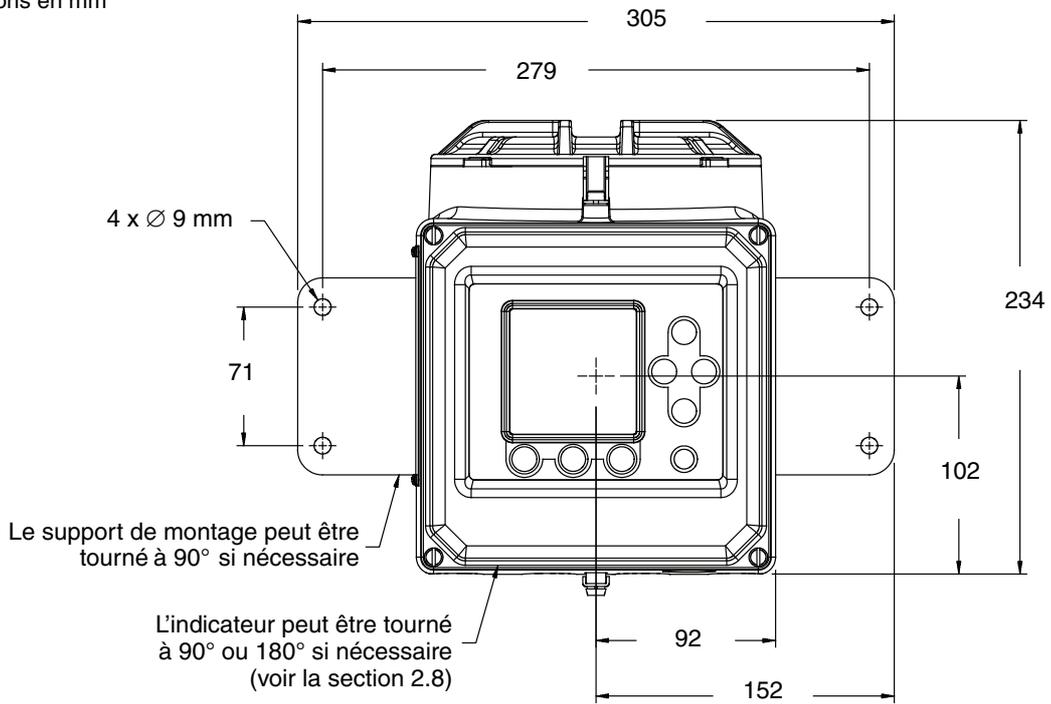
Dimensions du Modèle 3350 ou 3700 – vue de dessus
